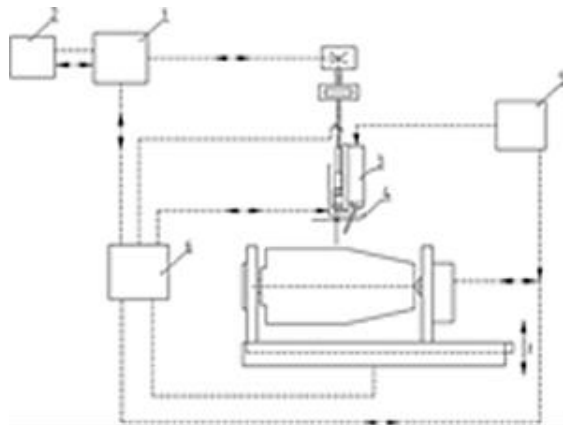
Принципиальная схема установки для комбинированной лазерно-дуговой сварки
